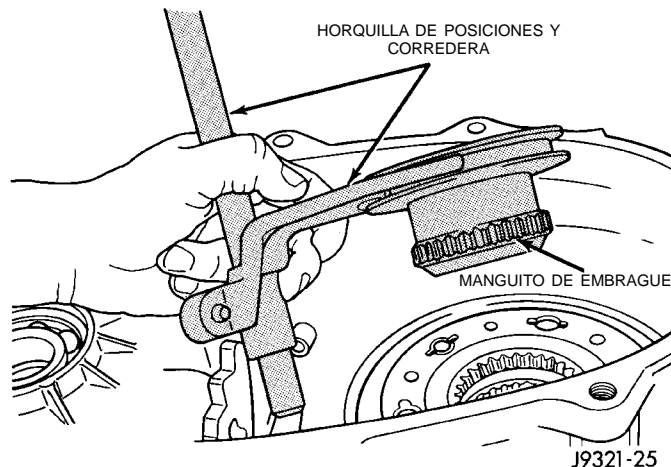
Desmontaje de la horquilla de posiciones y el manguito de embrague
